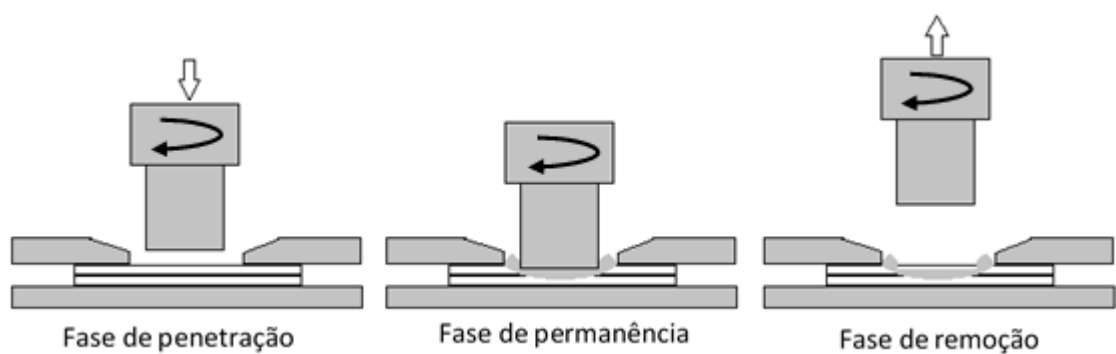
Produção de soldaduras por TAFSW
